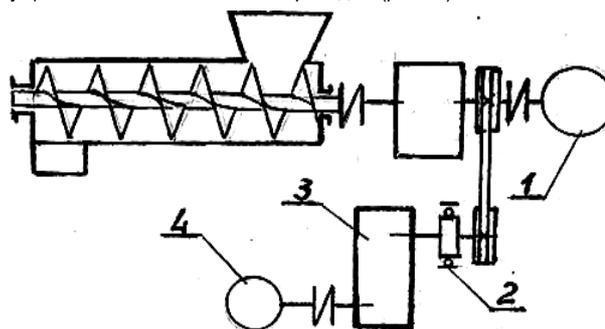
Схема вспомогательного привода: 1 – главный двигатель; 2 – обгонная муфта; 3 – редуктор; 4 – вспомогательный двигатель
